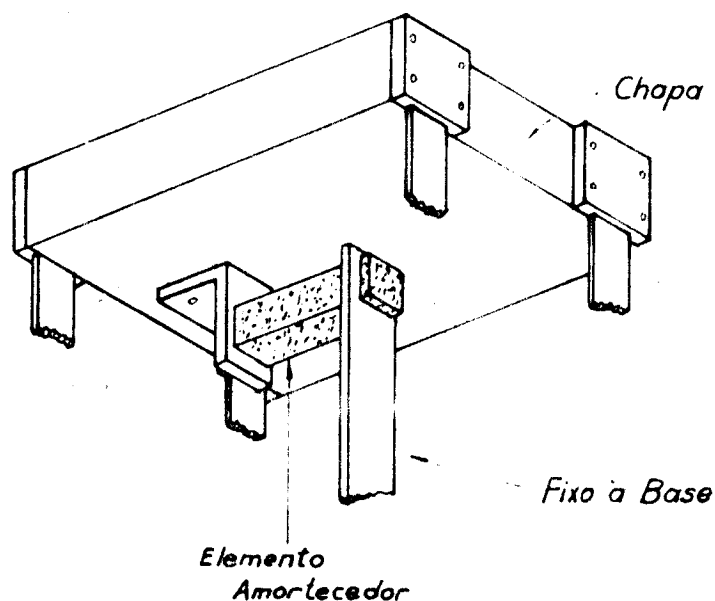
Detalhes da montagem do Elemento de Borracha.
